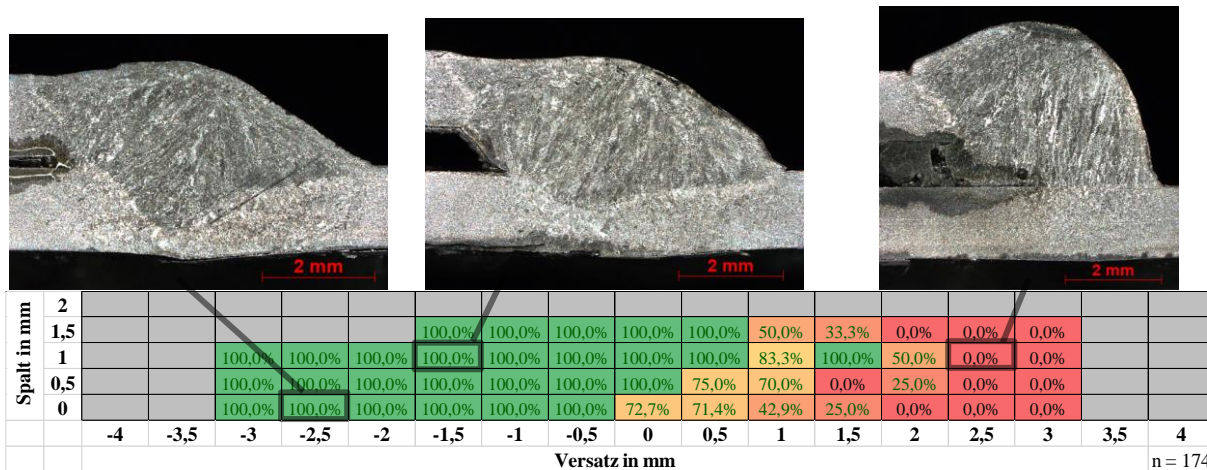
HX340LAD+Z140|CMT|C1 – Einbrandtiefe einschließlich Proben mit veränderter Probengeometrie
